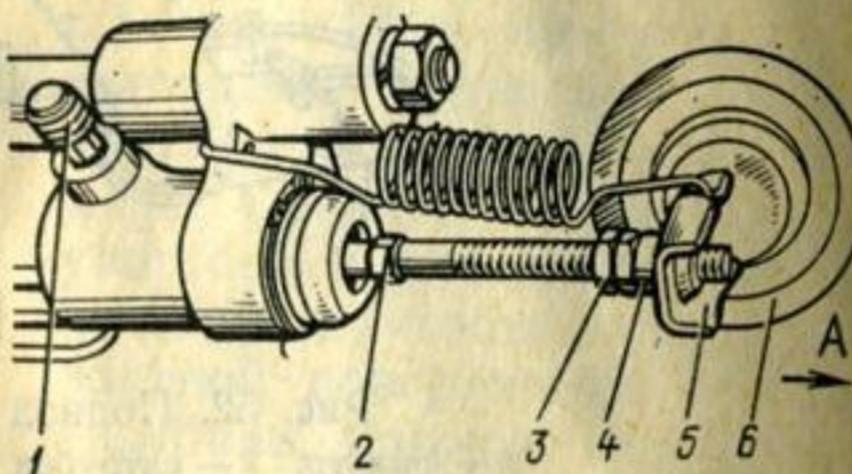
Регулировочный узел гидравлического привода сцепления:
